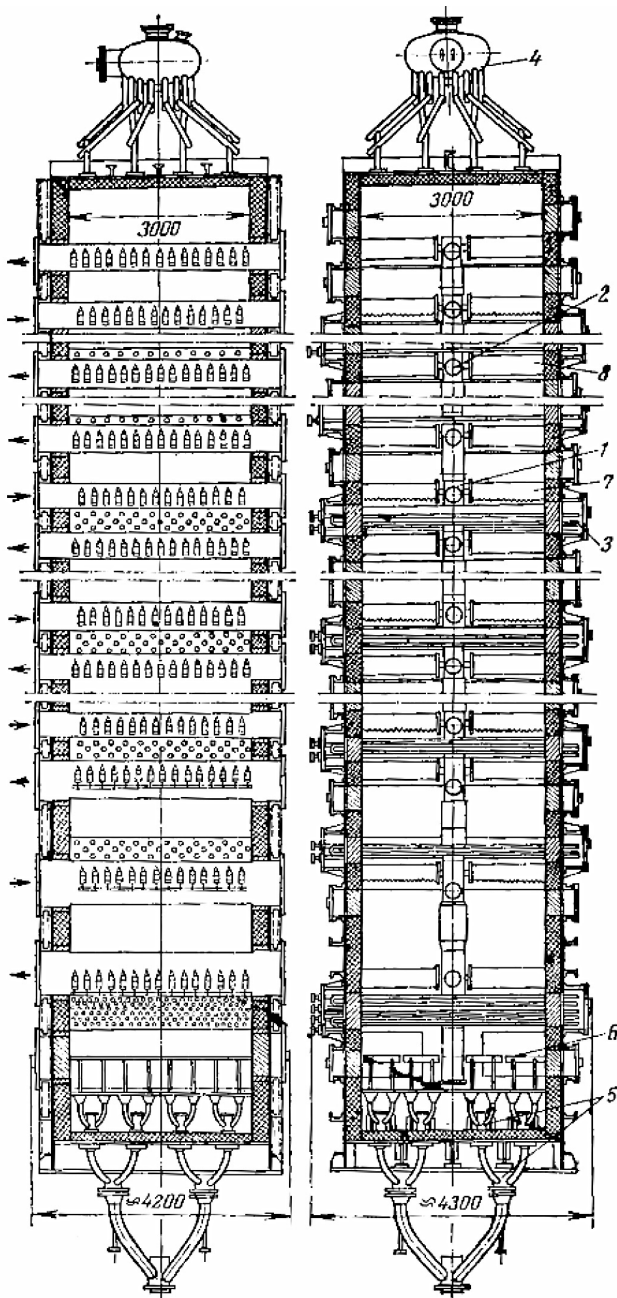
Регенератор установки каталитического крекинга с шариковым катализатором: 1 — коллектор ввода воздуха; 2 — коллектор вывода дымовых газов; 3 — охлаждающие змеевики; 4 — распределительное устройство; 5 — сборное выравнивающее устройство; 6 — колосниковая решетка; 7 — воздухораспределительный короб; 8 — газосборный короб
